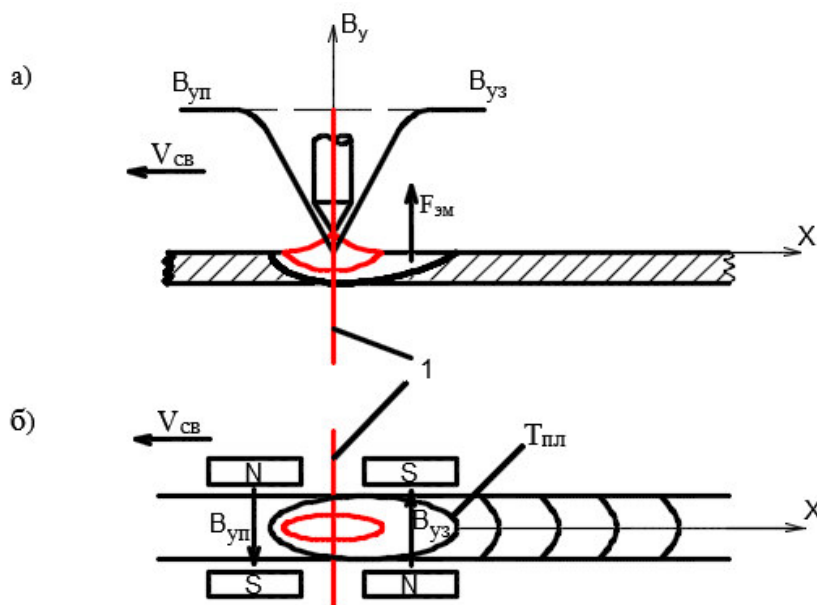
Дуга в квадрупольном магнитном поле при сварке немагнитных металлов при удержании сварочной ванны:
